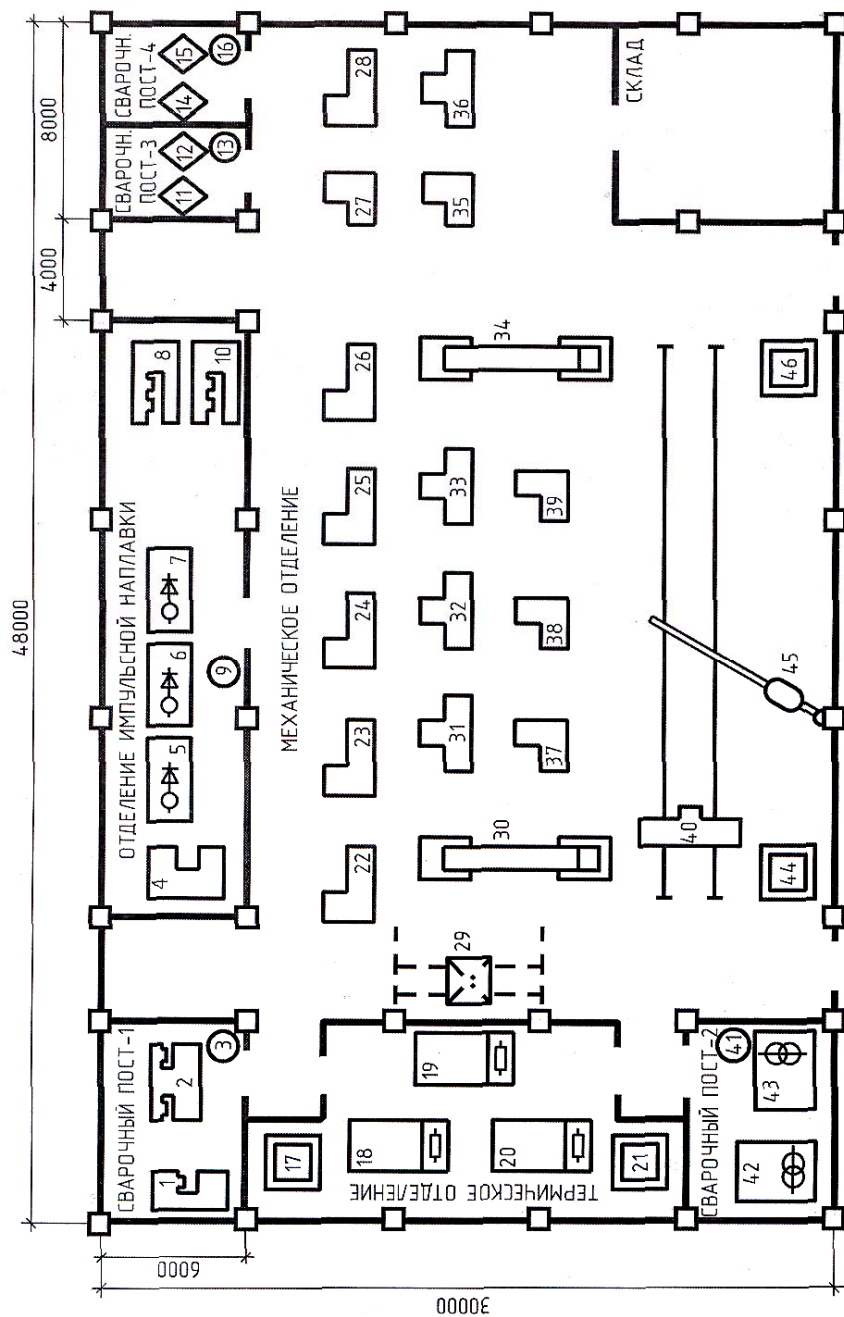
План расположения ЭО сварочного участка цеха
